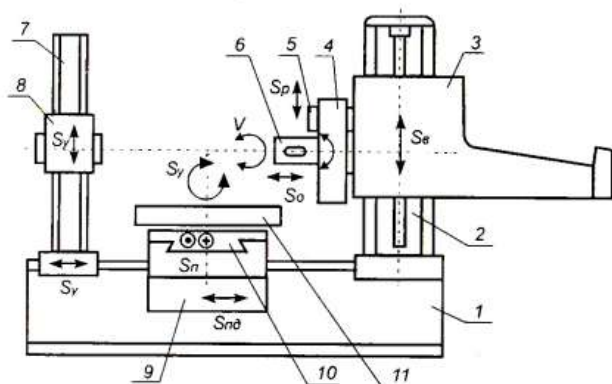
Загальний вигляд горизонтально-розточувального верстата
